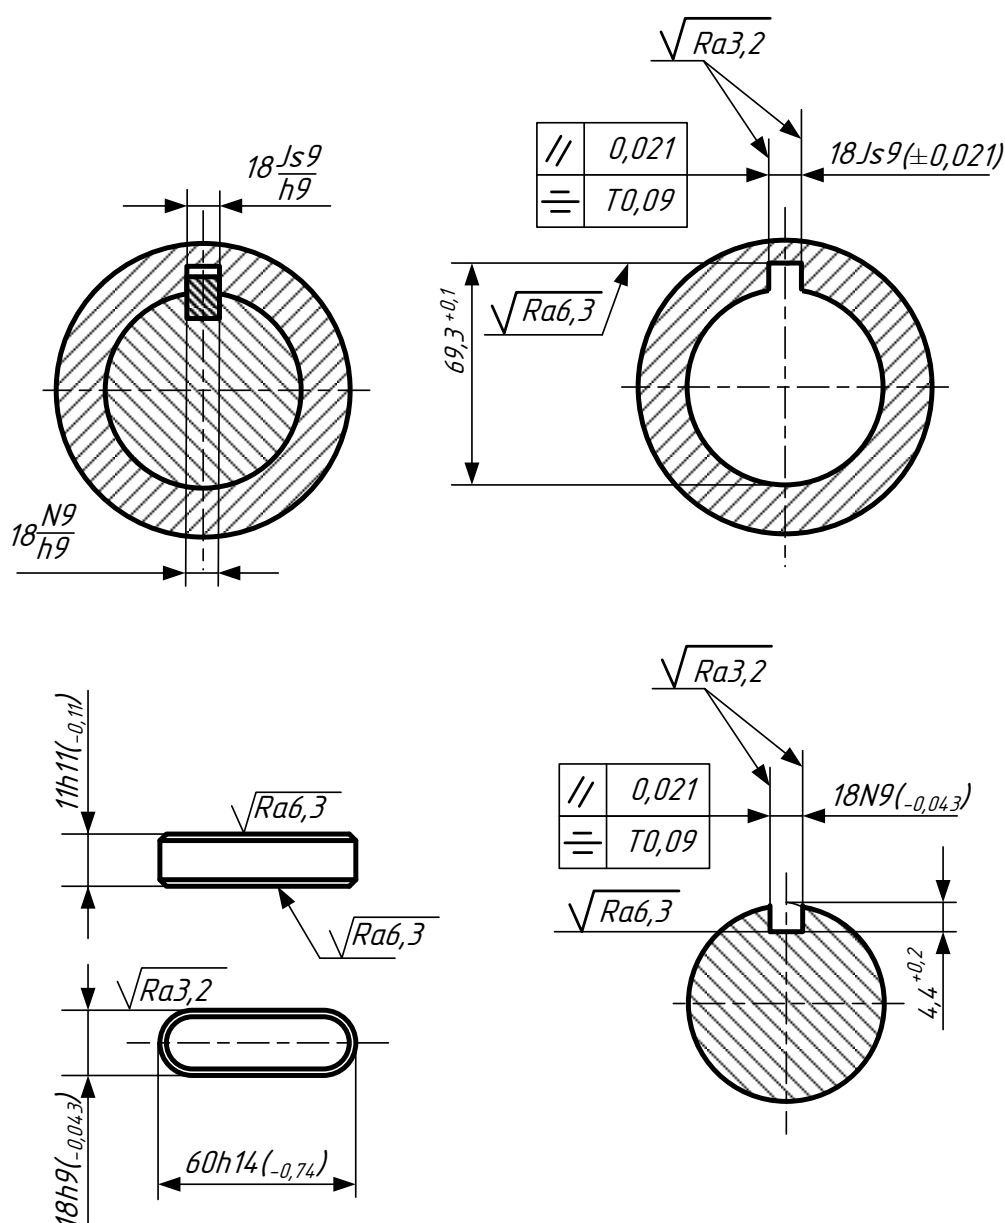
Эскизы шпоночного соединения и деталей
